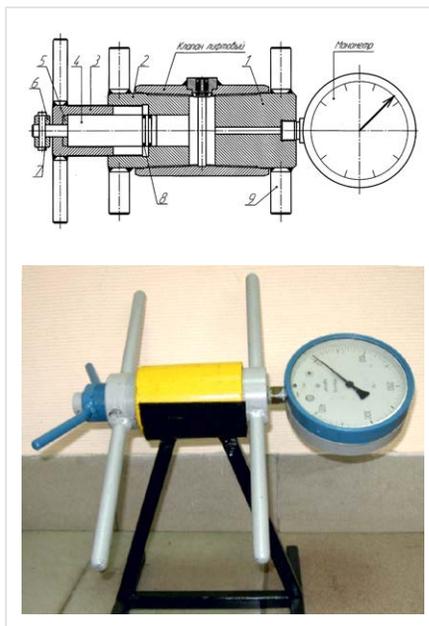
Стенд диагностики бывших в эксплуатации лифтовых клапанов: 1 — заглушка; 2 — корпус—цилиндр; 3 — силовой винт; 4 — поршень; 5 — кольцо опорное; 6 — кольцо верхнее; 7 — штифт; 8 — кольцо резиновое уплотнительное; 9 — рукоятка
